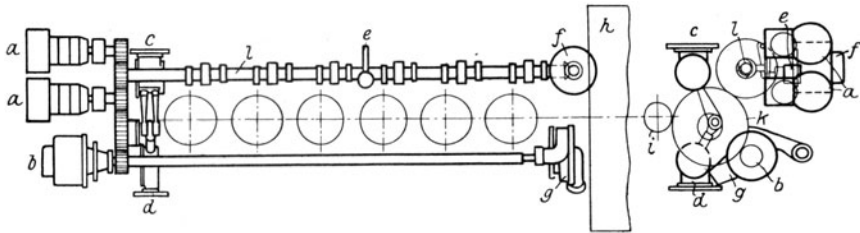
und 253. Maschine von 150 PS für Tanks. Schema des Antriebs der Hilfseinrichtungen.
